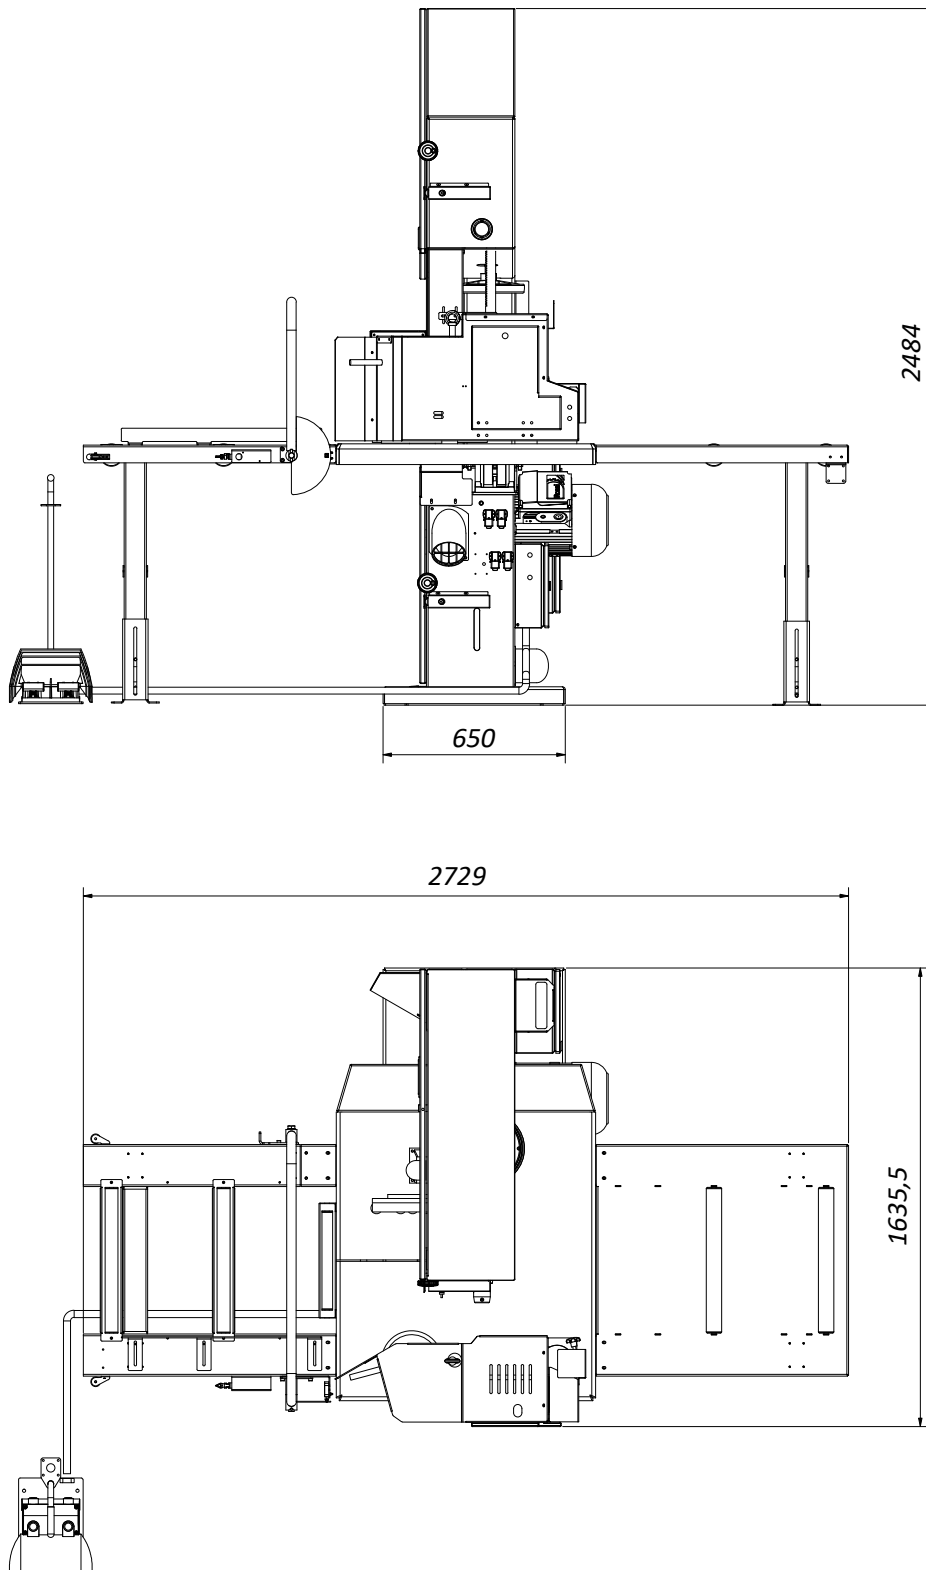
Seitenansicht und Draufsicht TBS 800 R
